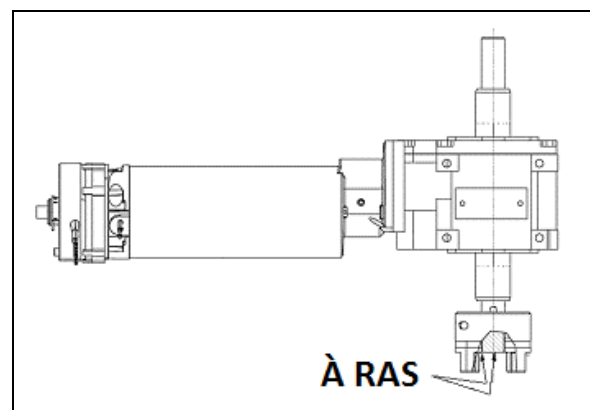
POSITION DU MOYEU DE SERRAGE SUR L'ARBRE DE LA BOÎTE D'ENGRENAGE 26047
